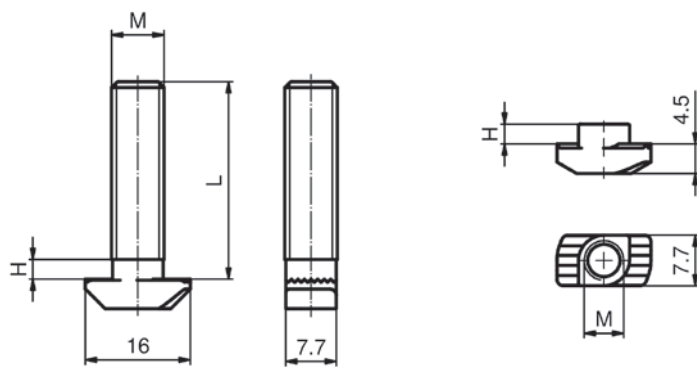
Abmessungen Hammerschrauben und Hammermuttern AXF
